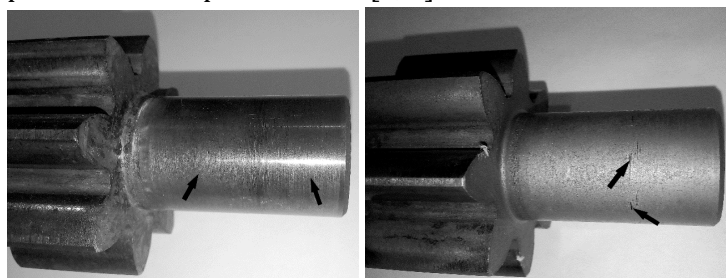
Следы износа посадочной поверхности цапфы шестерни шестеренного насоса НШ-32У: а - абразивное изнашивание; б - схватывание
